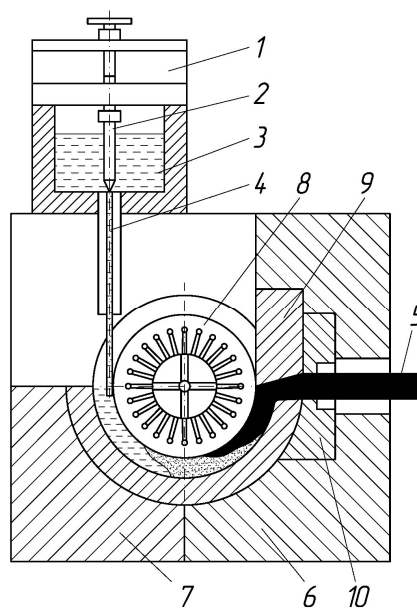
Схема установки Кастэкс: 1 – заливочный ковш; 2 – регулятор уровня; 3 – жидкий металл; 4 – напорная трубка; 5 – пресс-изделие; 6 – прижимной башмак; 7 – башмак для охлаждения расплава; 8 – колесо; 9 – упор; 10 – матрица
